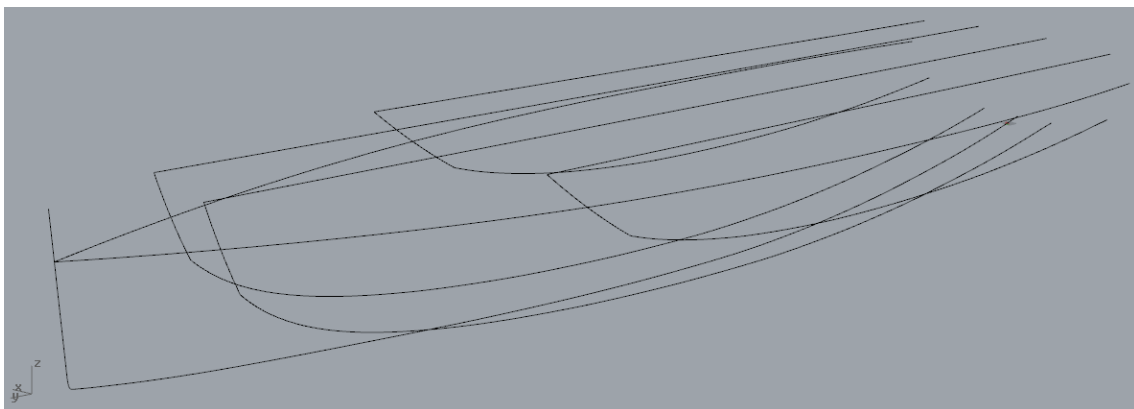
Disposición de refuerzos longitudinales. Editado con Rhinoceros
